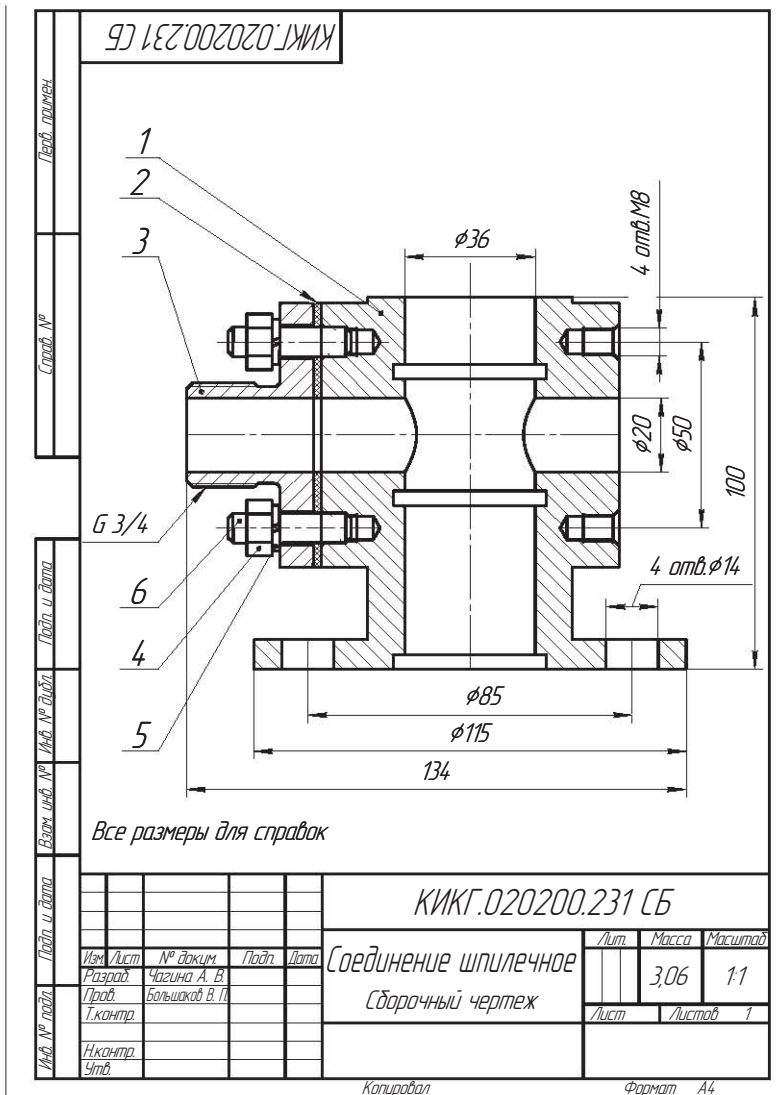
Ассоциативный сборочный чертеж соединения шпильчного
